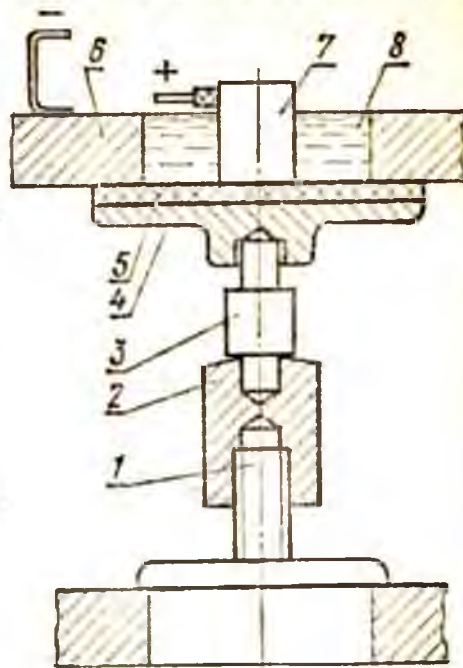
Відновлення поверхні посадочного отвору в корпусі коробки передач трактора: 1 - гвинт з фланцем; 2 - тайка; 3 - упорний стрижень; 4 - диск; 5 - ізоляційна (гумова) прокладка; 6 - корпус коробки передач (катод); 7 - анод; 8 - ванна в відновлюваному отворі.
